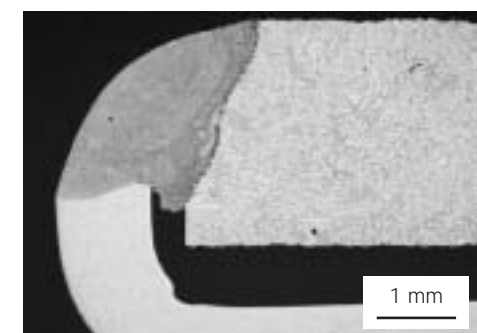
Querschliff einer lasergeschweißten Aluminiumguss-Blech-Verbindung
